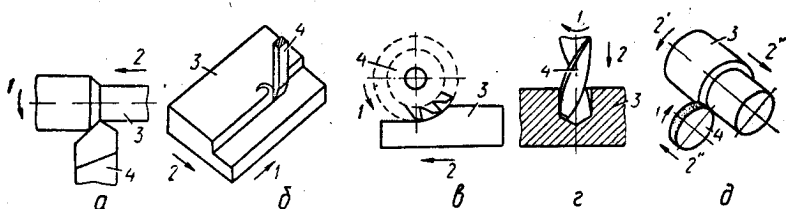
Типовые способы обработки металлов на металлорежущих станках
